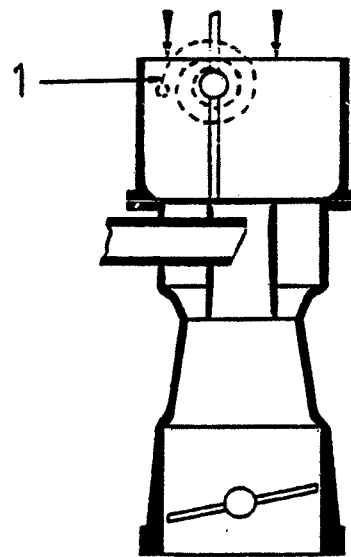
[2] — Carburatore munito di starter semiautomatico.
